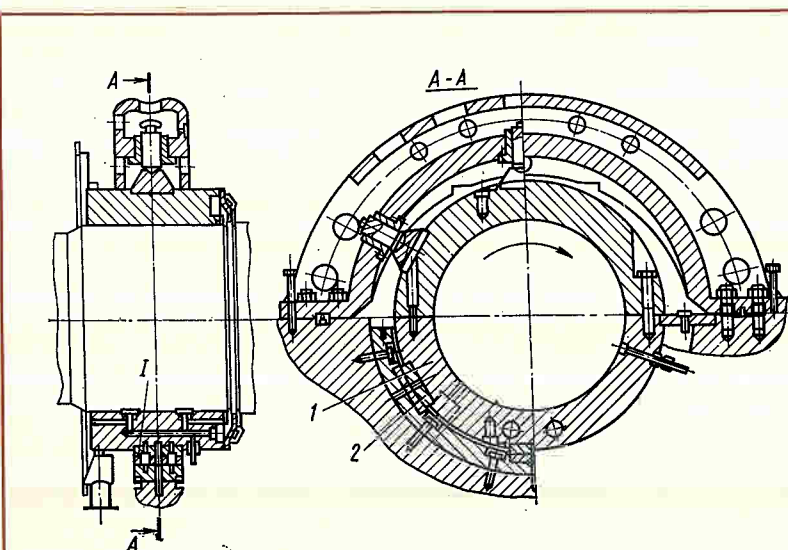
Разрез по опорному подшипнику 1 — сфера
